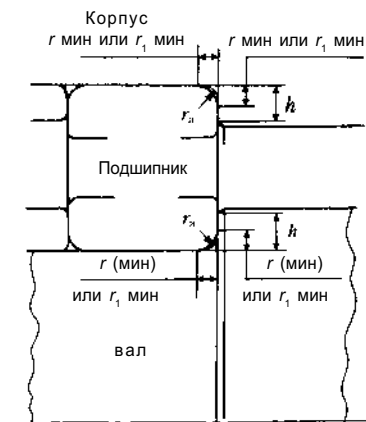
Размеры фасок, радиусы галтели вала и корпуса и высота заплечиков
